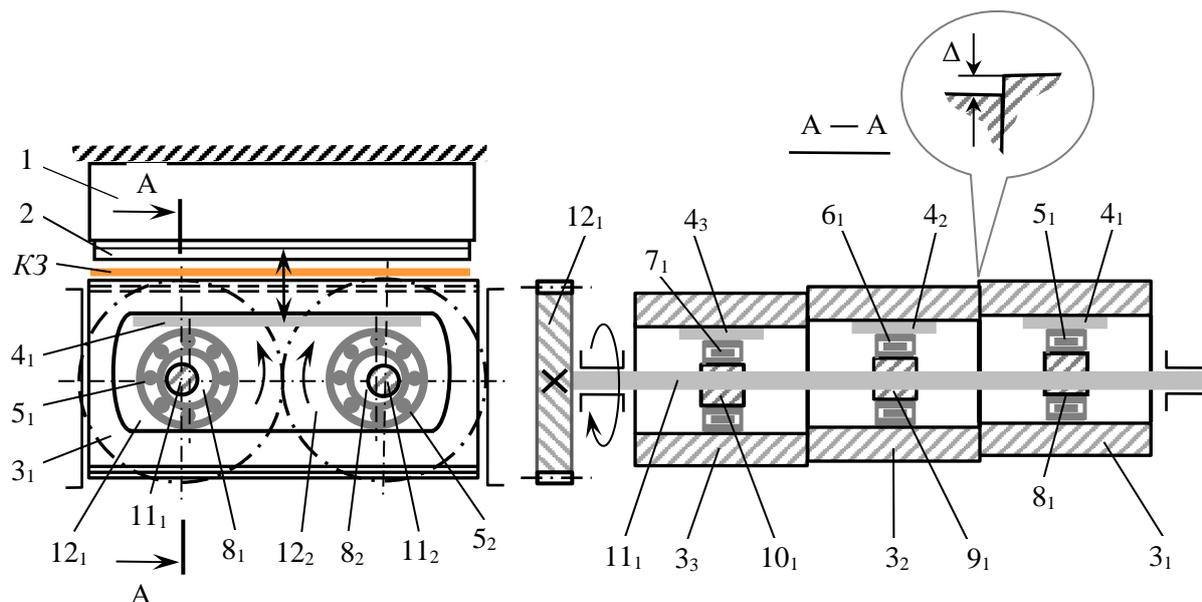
Схема штанцювального преса з ексцентриковими механізмами привода натискної плити секційної будови
